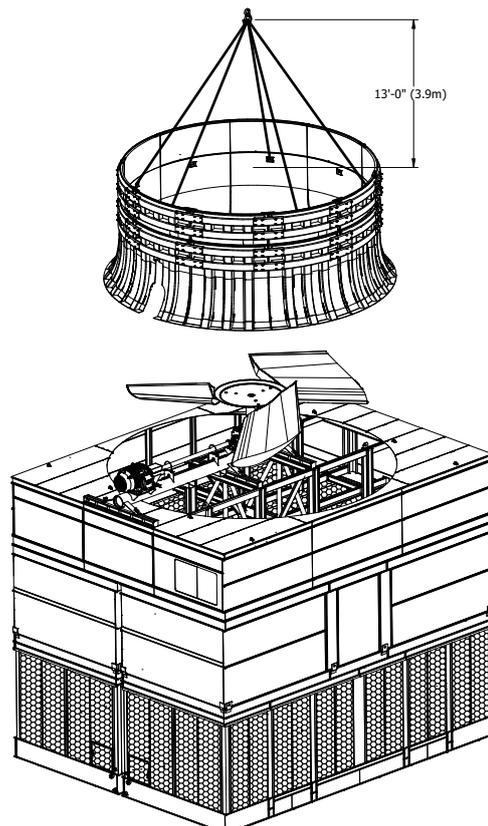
Monage des Zylinders (extra geräuscharmer Ventilator)
